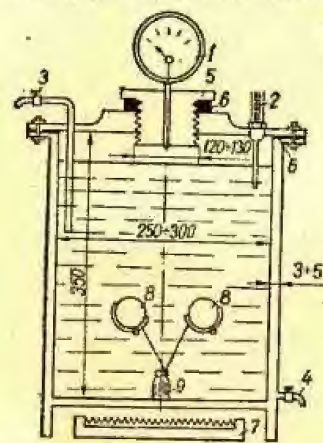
Установка для проверки герметичности поплавков и контактов;
